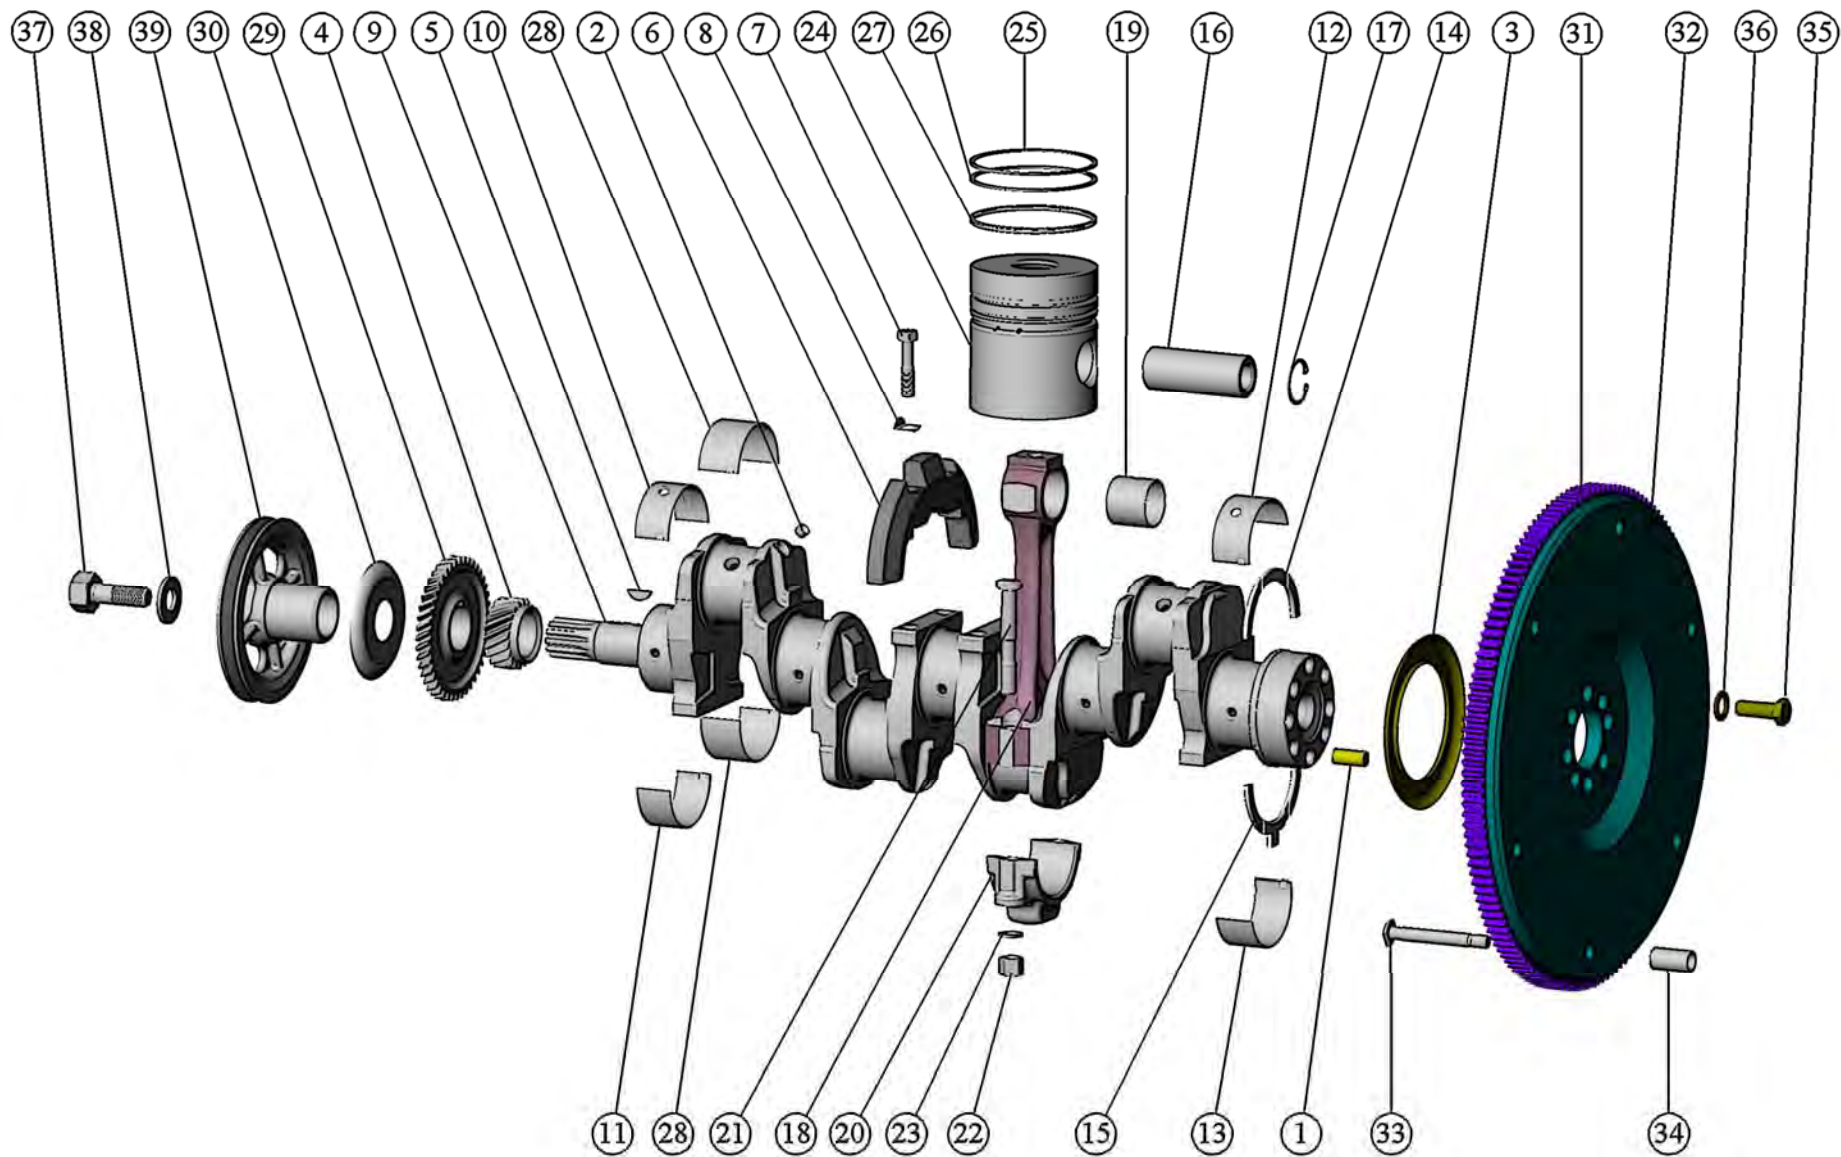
Кривошипно-шатунный механизм. Установка маховика. Установка шкива коленчатого вала.
